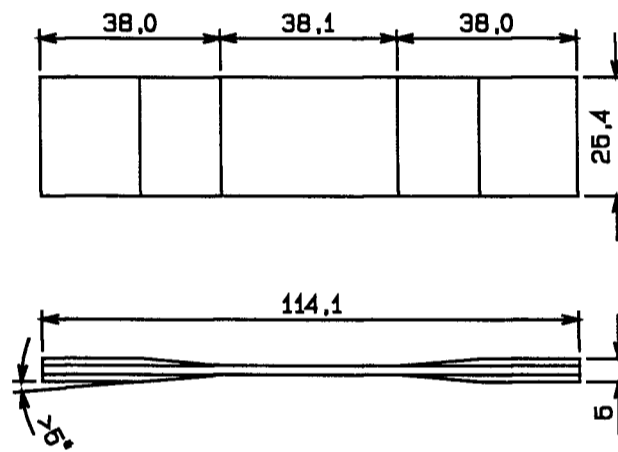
Geometria e dimensões do corpo-de-prova de tração transversal.
